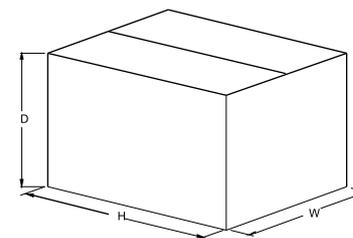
Габаритные размеры упаковочной тары
